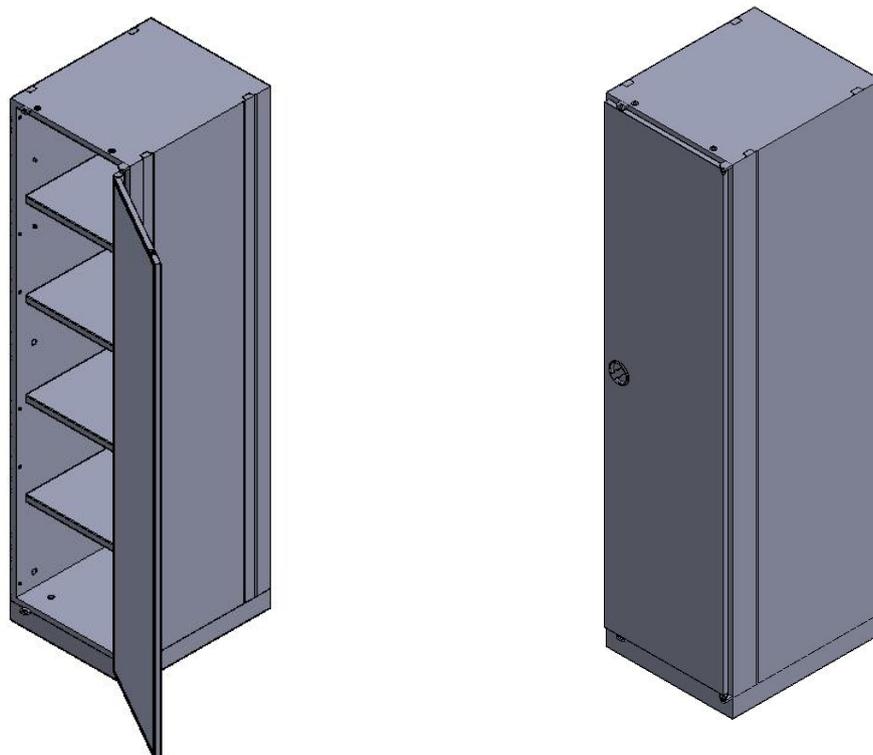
Edelstahl-Hochschrank Typ 528 komplett mit vier Einlegeböden
